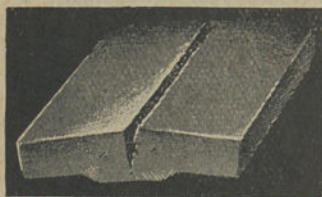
Ruptura duma soldadura apresentando causa de fractura, após o ensaio de dobra.
